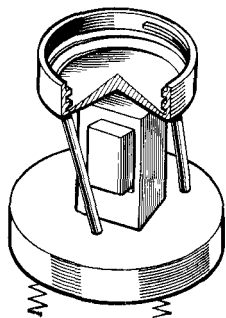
Бункер для захвата и ориентации потока заготовок
